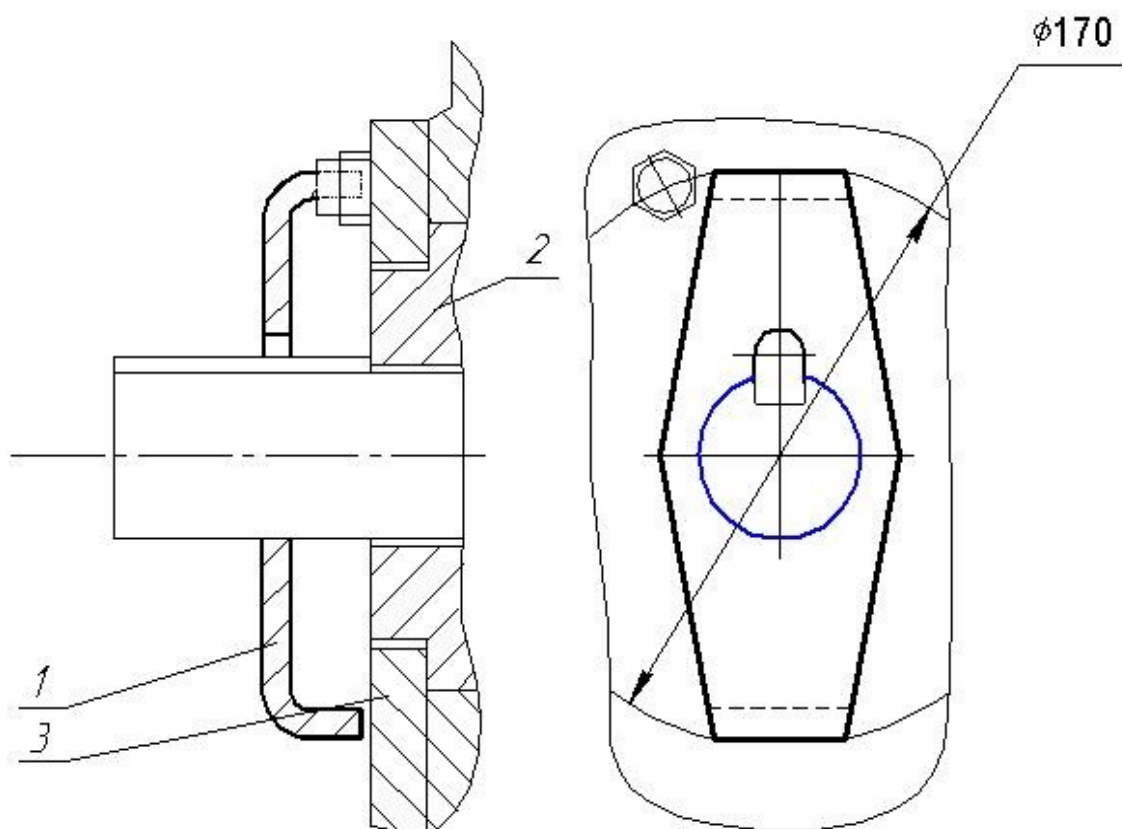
Приспособление для съема радиально-упорных подшипников
